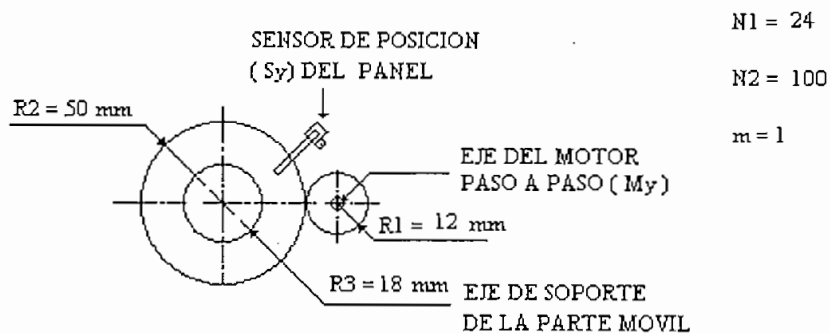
Grupo de engranajes acoplados al motor M_y
